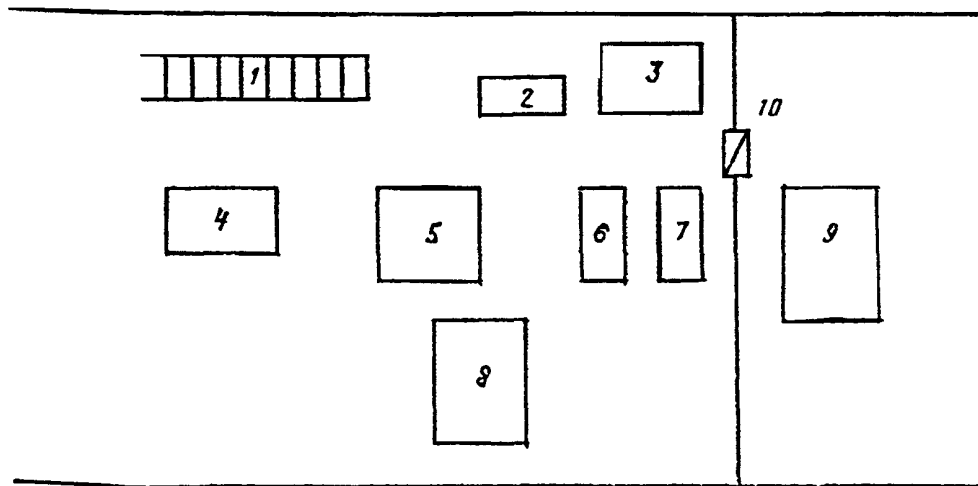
Типовая схема организации рабочего места разборки коробки передач:
